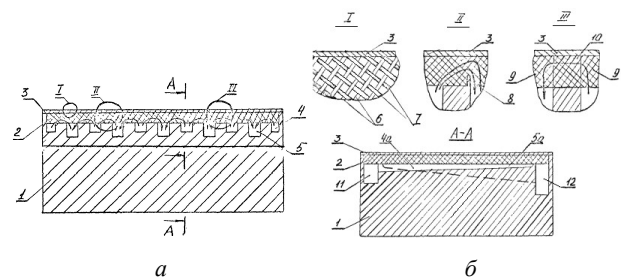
Схемы некоторых конструктивных решений СО с перетоком: 1 – основа; 2 – пакет охлаждения; 3 – подложка; 4 – раздаточный канал (может быть сужающимся – 4а); 5 – сборный канал (может быть расширяющимся – 5а); 6 – проволоки утка; 7 – проволоки основы; 8 – ребро; 9 – области с повышенной пористостью; 10 – область с пониженной пористостью; 11 – раздаточный коллектор; 12 – сборный коллектор.
